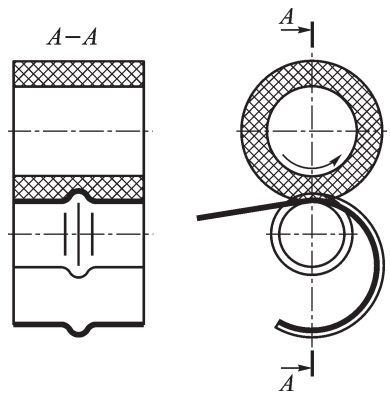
Схема операции формовки листовой заготовки на валках с эластичным покрытием
